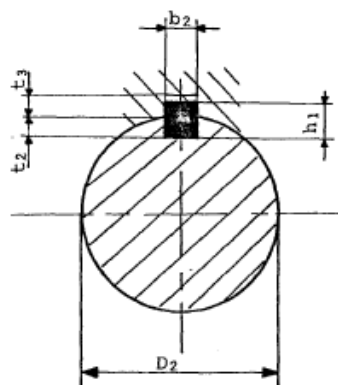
DIMENSIONAMIENTO DE LA CHAVETA.
